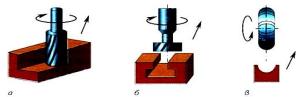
Виды фрез: а, б — концевые; в — фасонная
